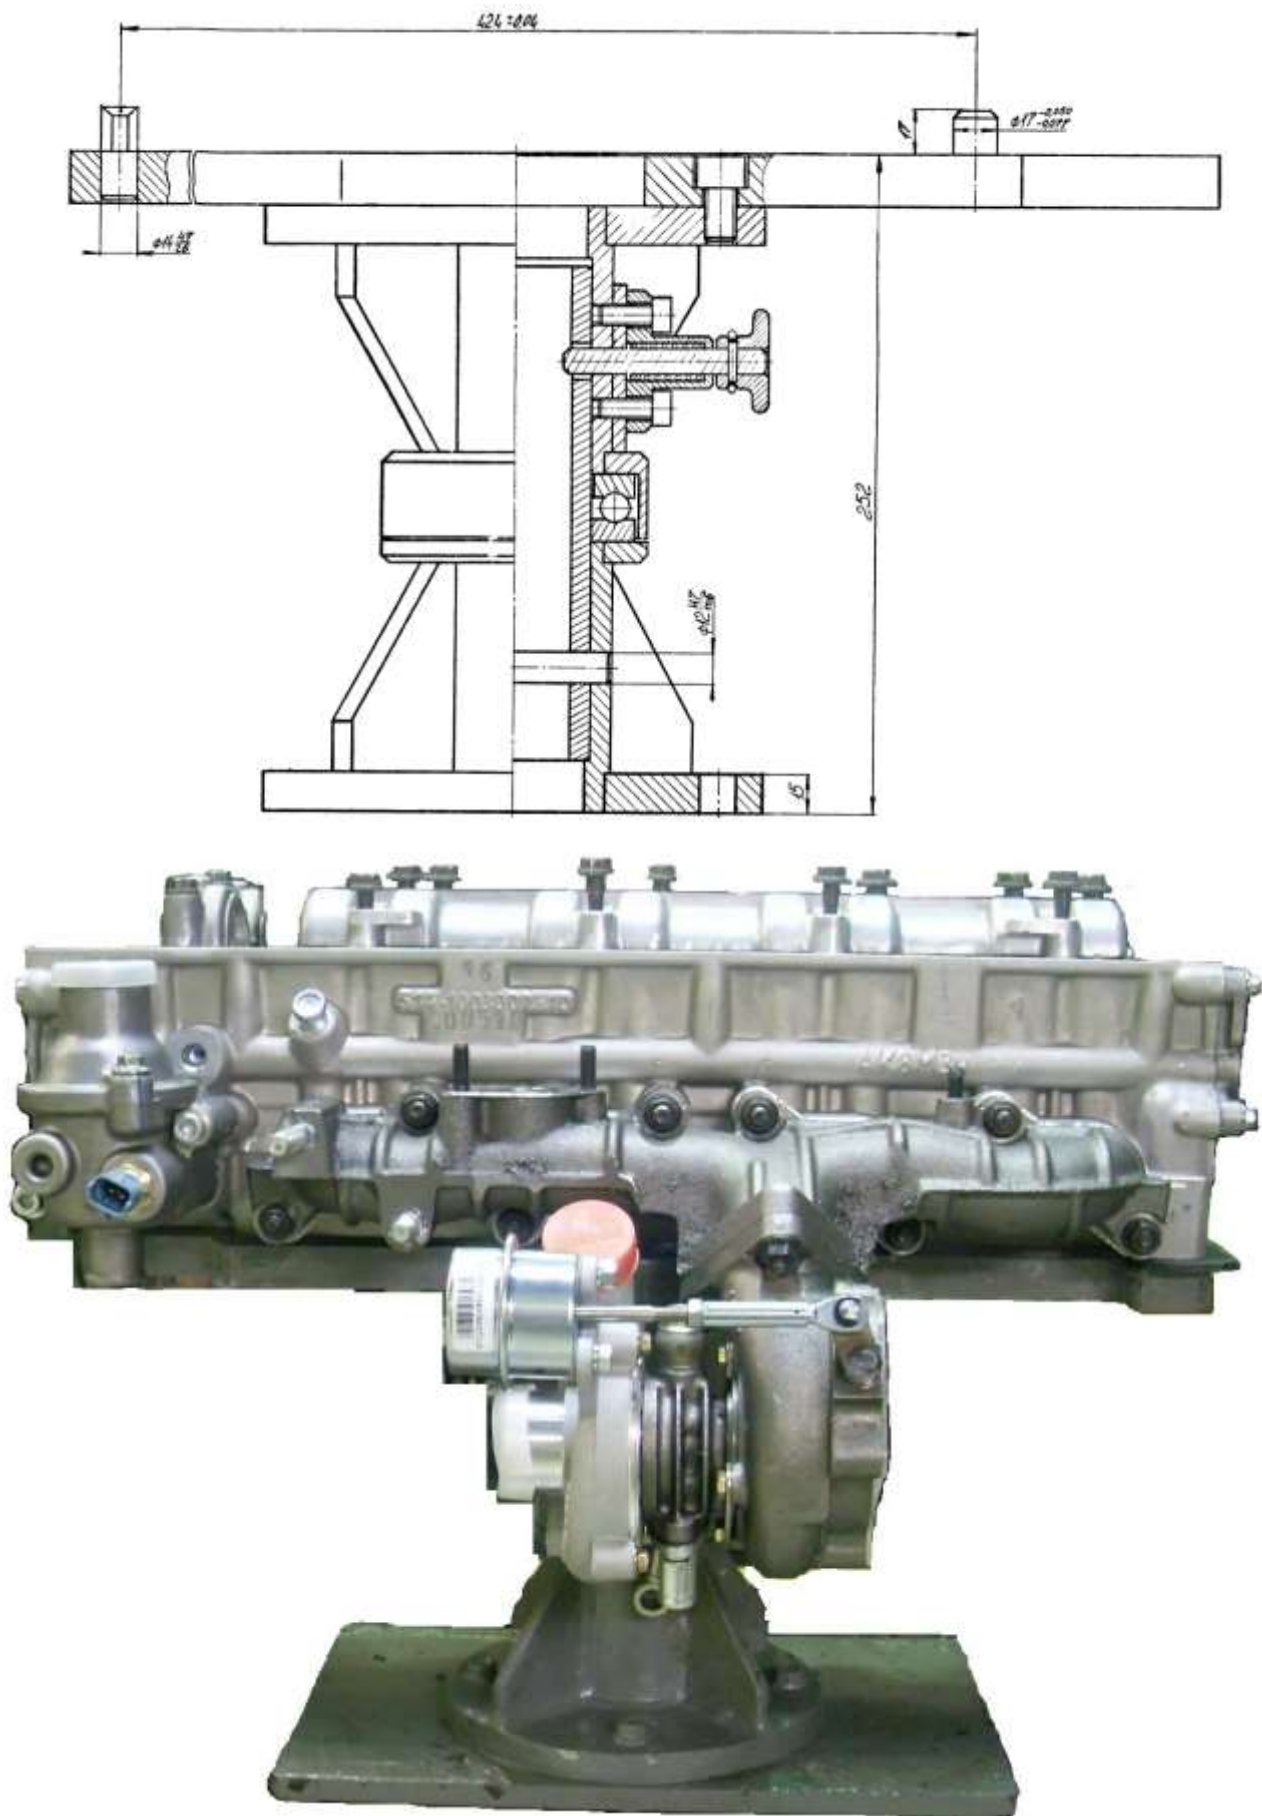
ЗМ 7823-4662 Подставка поворотная для подбора ГБЦ
